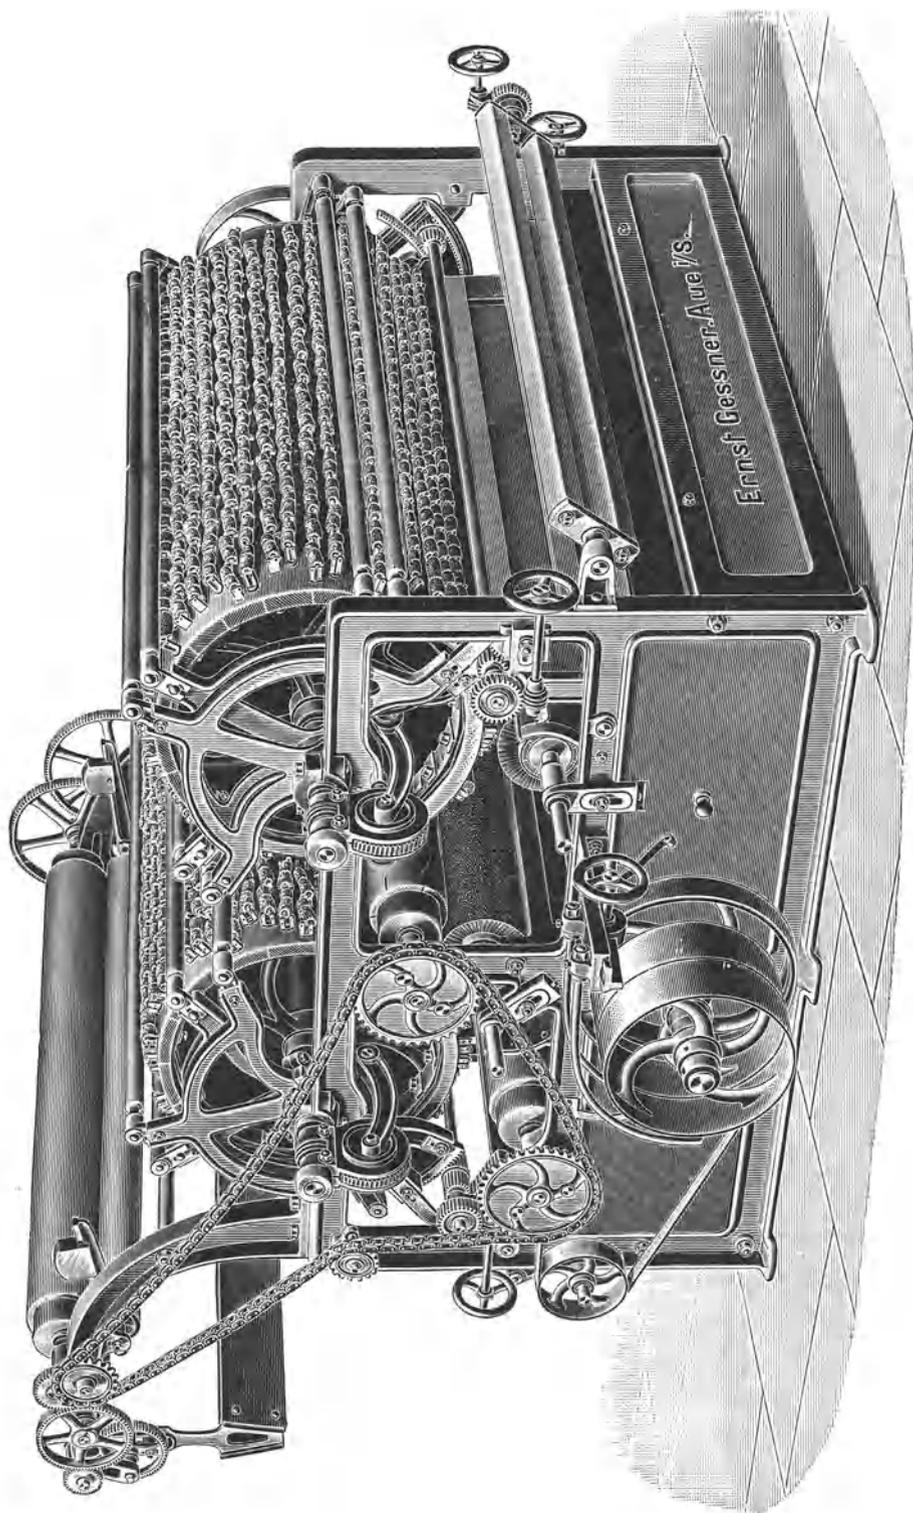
Raubmaschine mit zwei großen Tambouren von Gessner.
